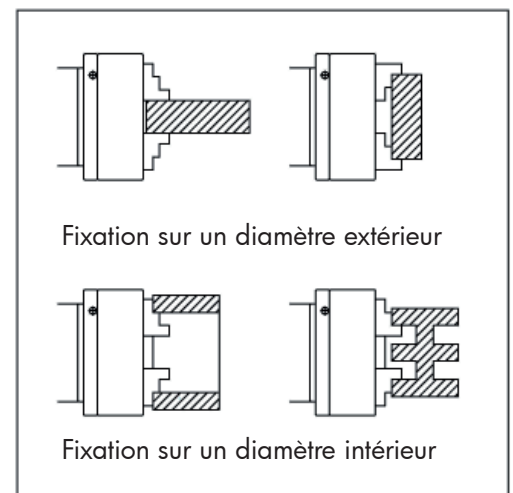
Exemples de pièce montée dans un mandrin à 3 mors
